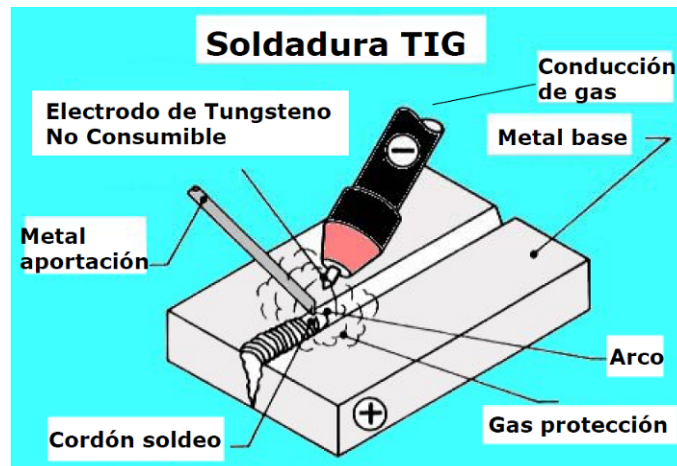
Proceso de realización de una soldadura mediante el procedimiento TIG [28].
